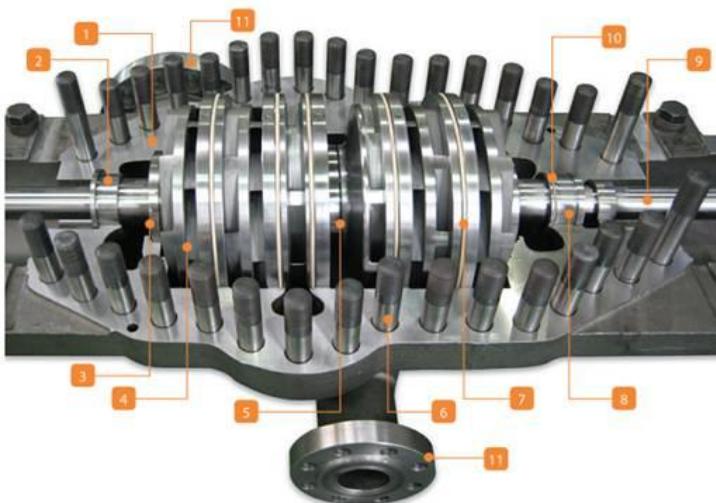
Основные детали насоса для перекачки нефтепродуктов (типа ВВЗ): 1 – корпус насоса; 2 – снижающая давление втулка; 3 – рубашка рабочего колеса; 4 – рабочее колесо с диффузором первой ступени; 5 – балансирующая диафрагма; 6 – крепежные шпильки; 7 – щелевое уплотнение диффузора; 8 – опорный болт; 9 – вал; 10 – уплотнение упорного болта; 11 – патрубок
